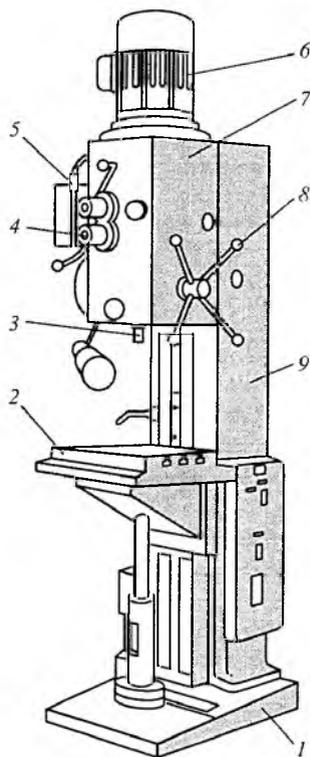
Вертикально-сверлильный станок мод. 2Н118:
